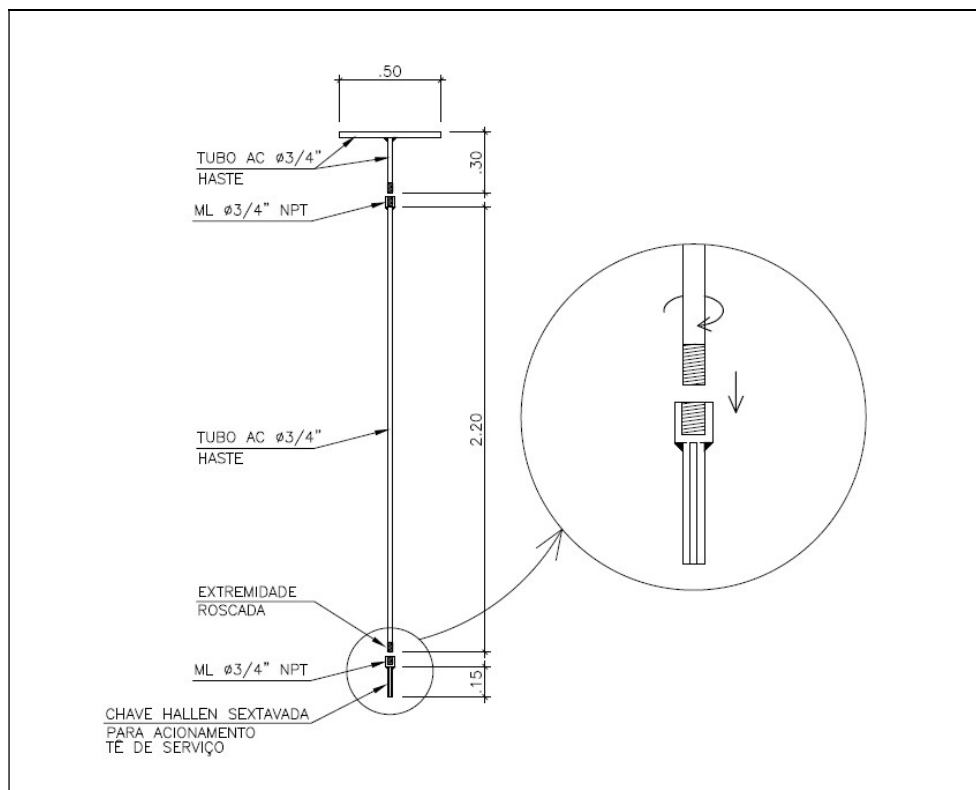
Dispositivo prolongador para furo de Te de Serviço
